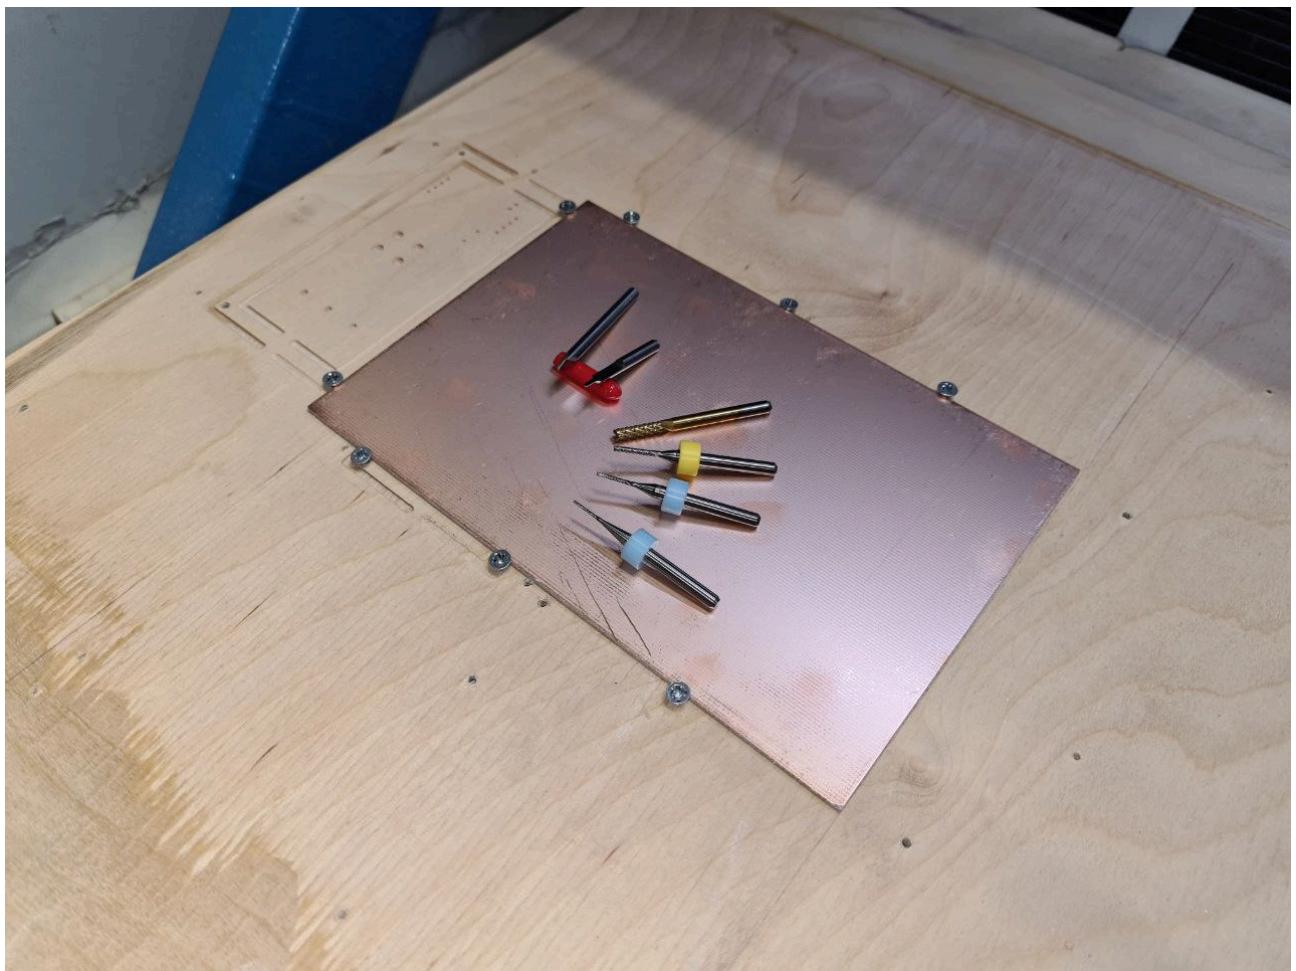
Крепление заготовки к столу и используемая оснастка
